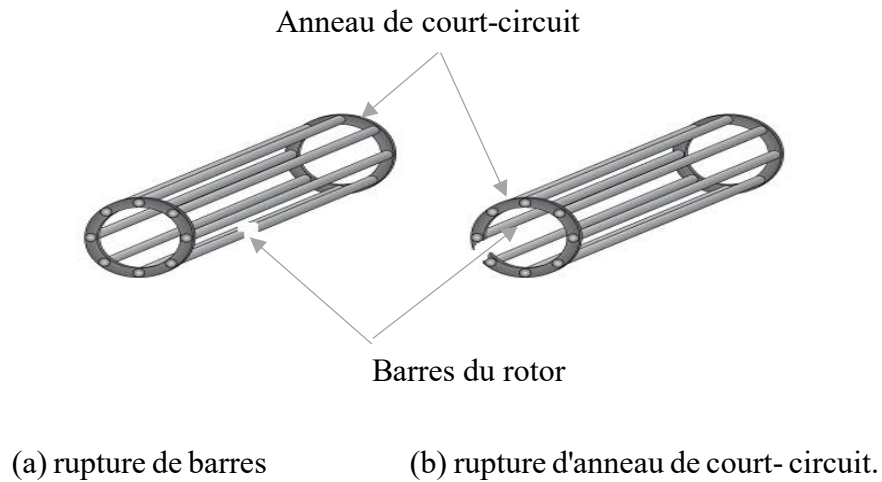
Défaut d'un rotor à cage d'écureuil[47].
